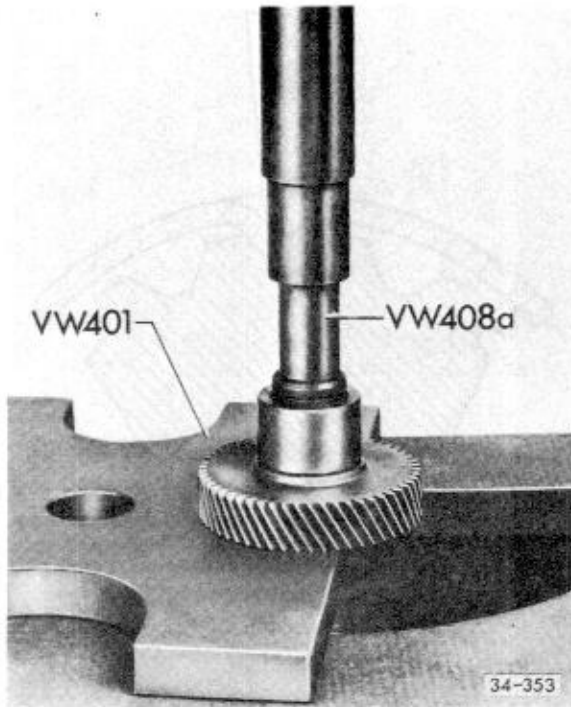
Zahnrad für 3. Gang mit Innenlaufring/Nadel-lager abpressen
